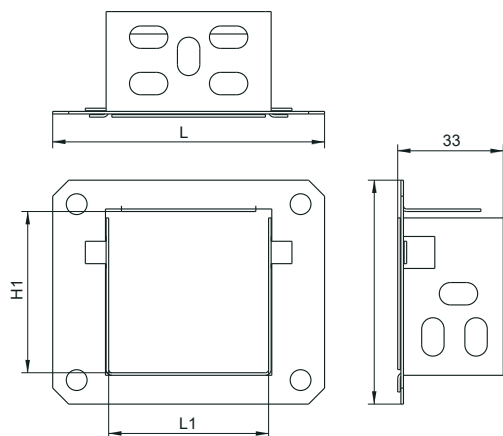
Фланец соединительный / Figure B.1 – Connecting flange
